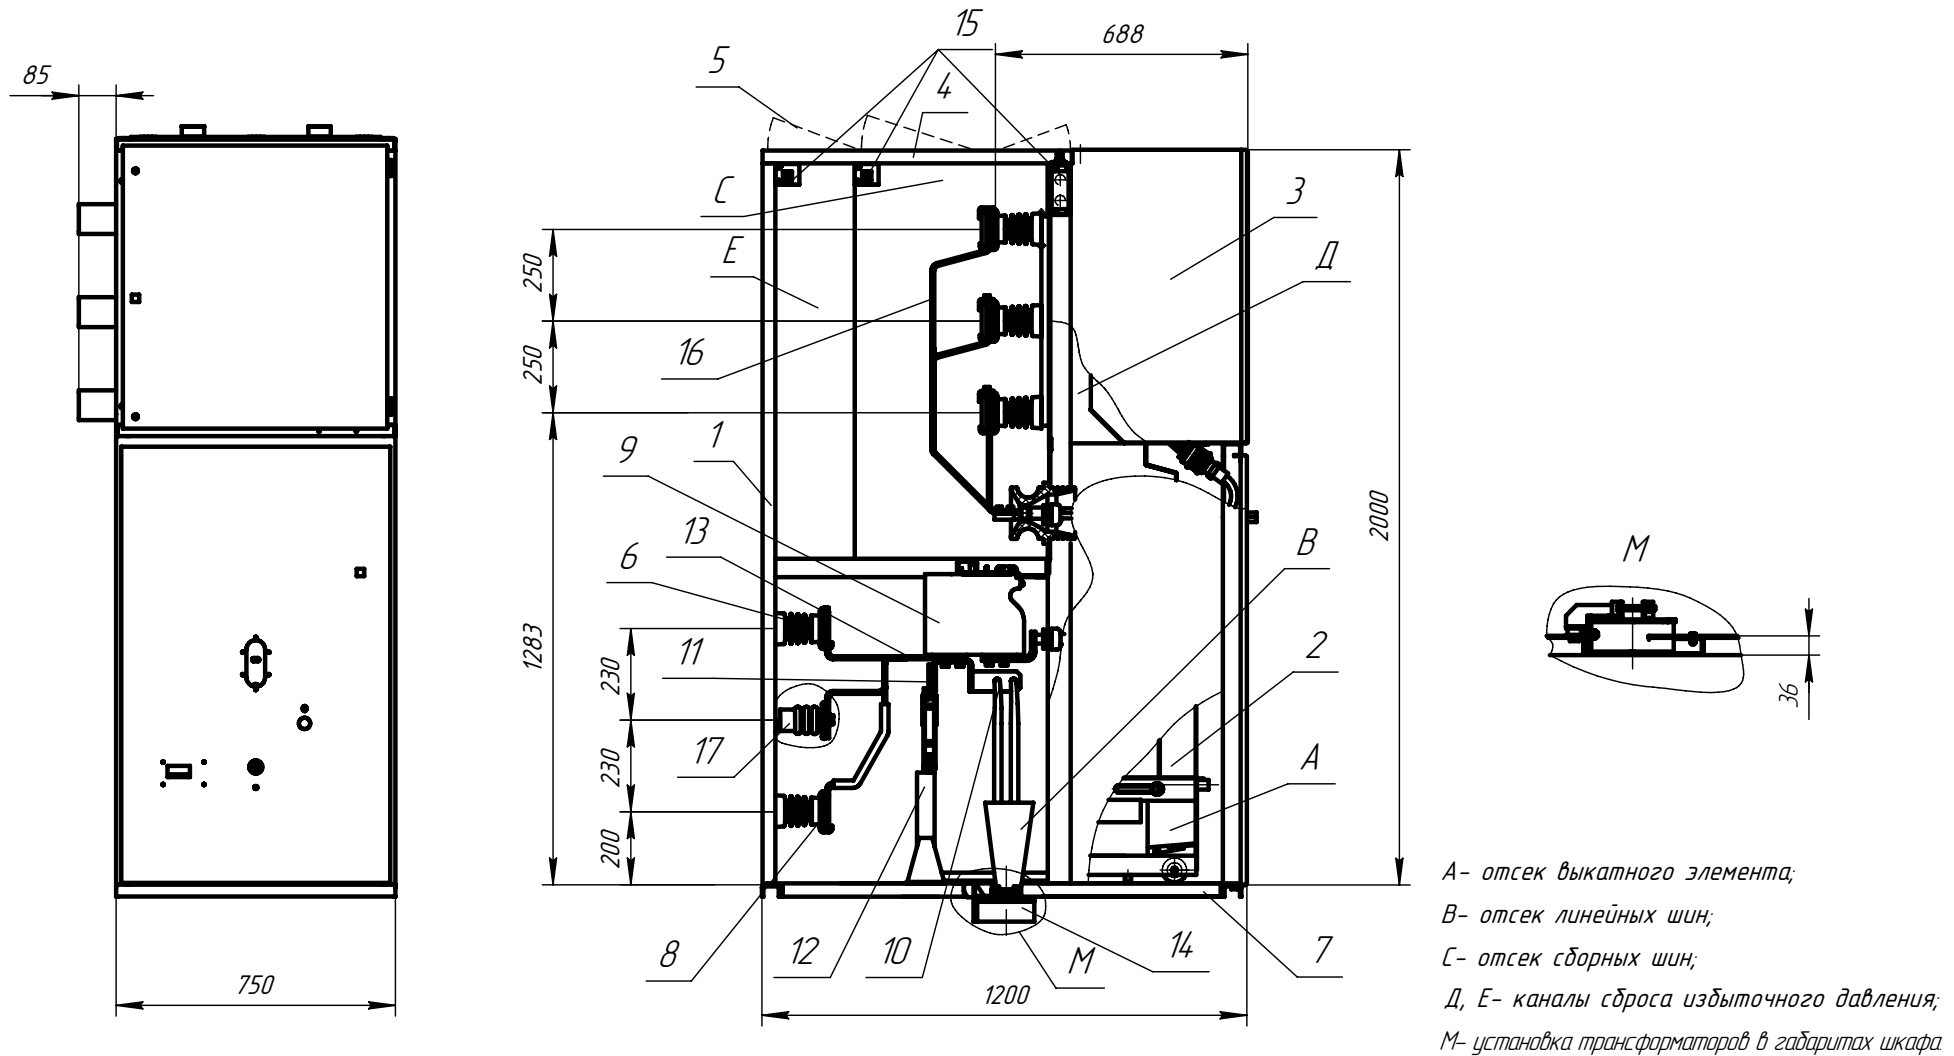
Габаритные, установочные, присоединительные размеры шкафов.
